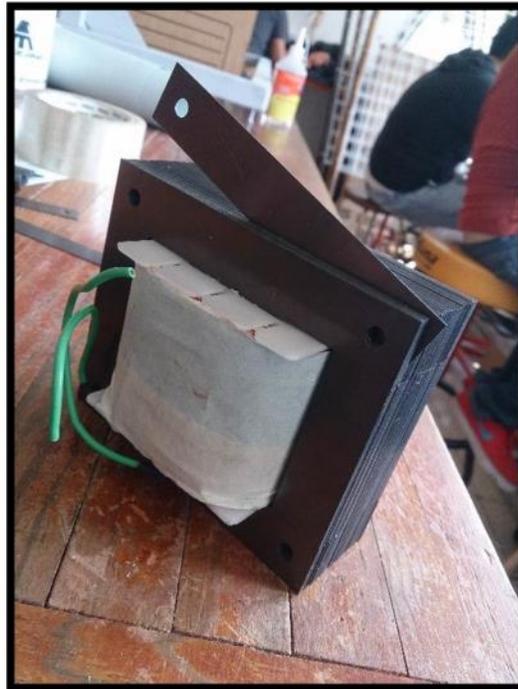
Devanado secundario cubierto con papel parafinado.
